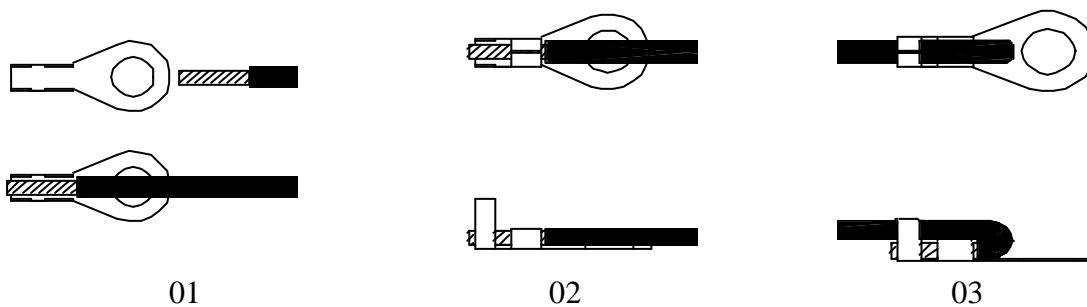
Detalle de conexión de cable con batería (C2 con C6 y C3)
